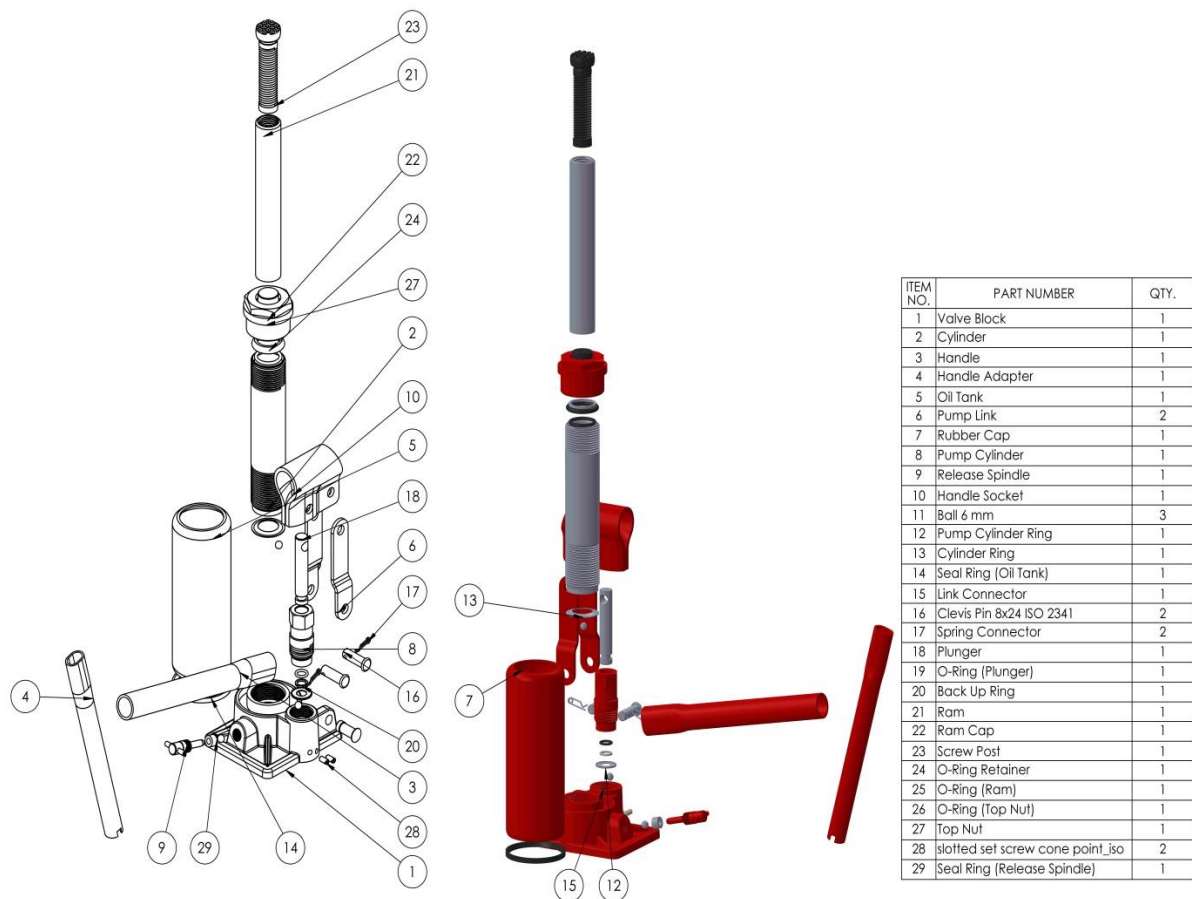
Dessin d'assemblage de presse hydraulique présenté par solide works
